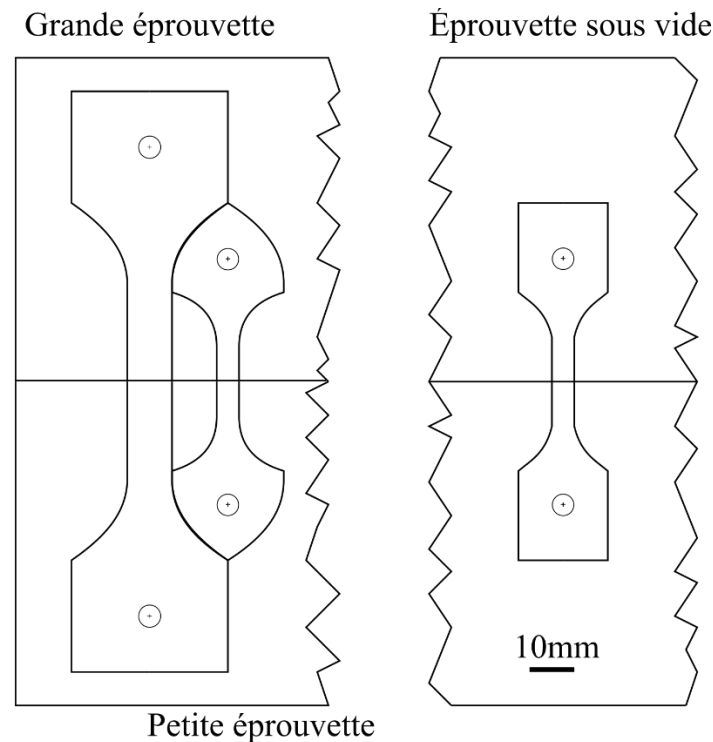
Épreuves au sein du coupon soudé.
